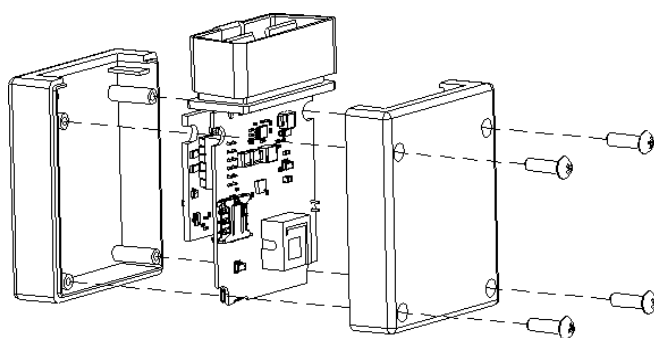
Вскрытие корпуса терминала (310 – слева; 312 – справа; 311 -снизу)
